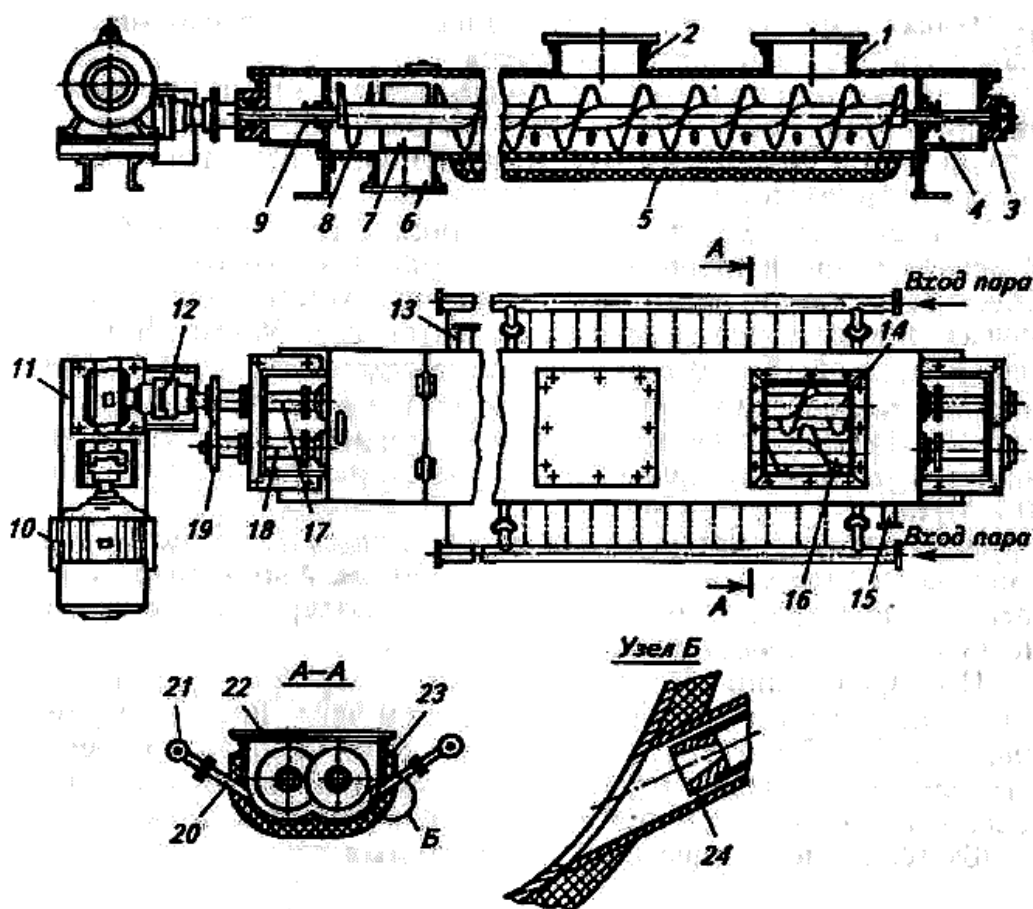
Групповой шнековый инактиватор: 1 — приемный патрубок; 2 — патрубок для выпуска избытка паров; 3 — подшипники; 4, 9 — сальниковые уплотнения; 5 — паровые трубы; 6 — выпускной патрубок; 7 — разгрузочные крыльчатки; 8 — шнек с обратной навивкой; 10 — электродвигатель; 11 — редуктор; 12 — муфта; 13 — патрубок для отвода конденсата; 14, 16 — спаренные шнеки; 15 — патрубок для подвода пара; 17, 18 — шнековые валы; 19 — зубчатая передача; 20 — форсунка; 21 — коллектор; 22 — крышка инактиватора; 23 — спаренный желоб; 24 — сопло
